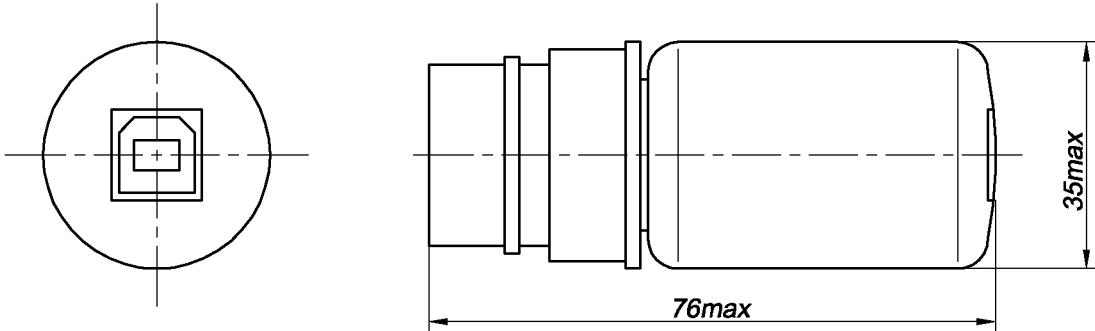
Внешний вид и размеры контроллера USB-1W
